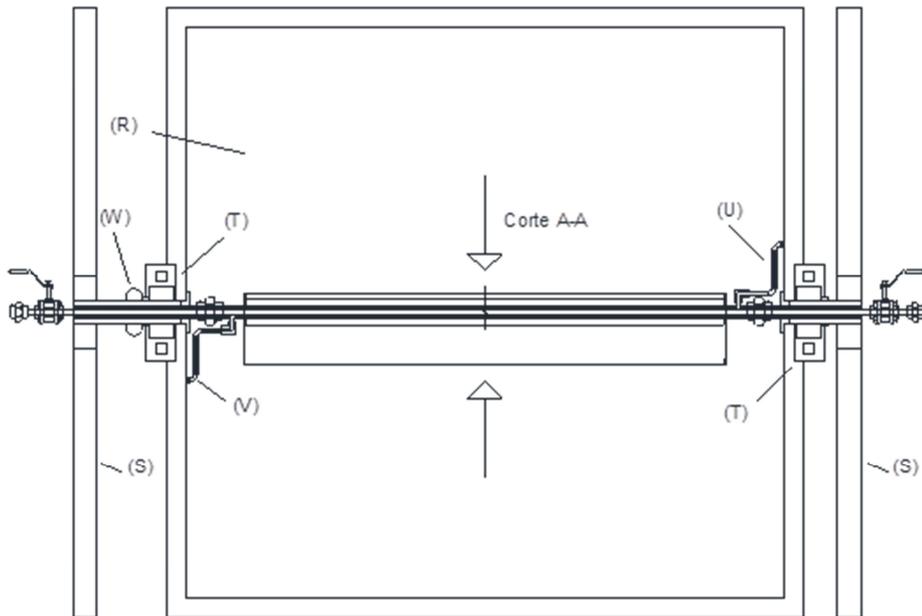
Muestra una vista en planta del dispositivo de la invención. Planta del Colector Solar con almacenamiento de energía térmica montado sobre un concentrador cilindro parabólico. Reflector cilindro parabólico (R). Soporte (S) vinculado al tubo intermedio del colector. Rodamientos de giro (T). Conducto (U) de ventilación de espacio anular donde se aloja el fluido de transferencia térmica. Conducto (V) de alimentación de fluido de transferencia térmica. Sistema de transmisión de giro (W).
